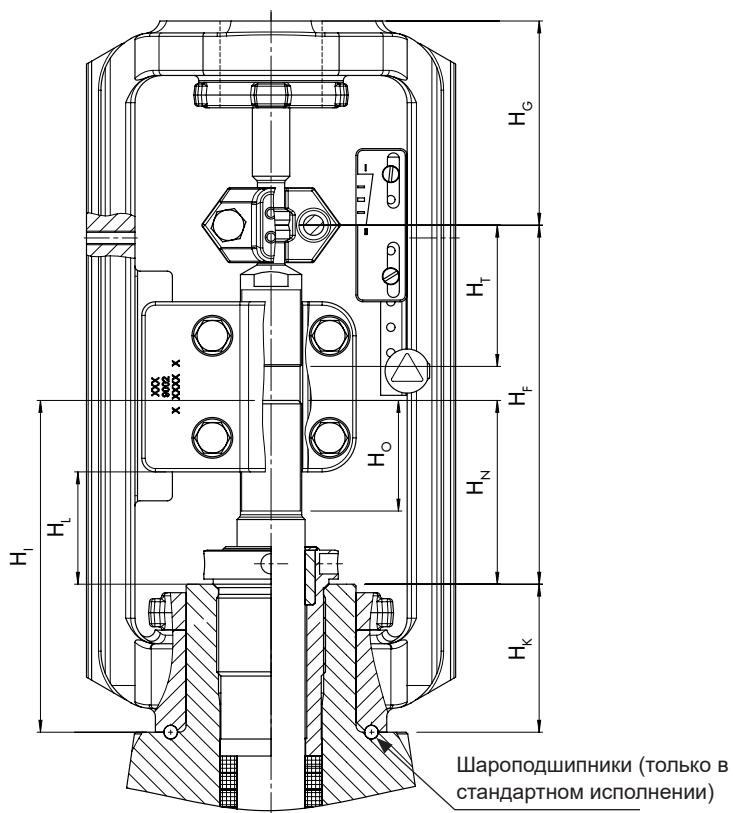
Габаритный чертёж с установочными размерами для пневматических приводов Тип 3271 и 3277
